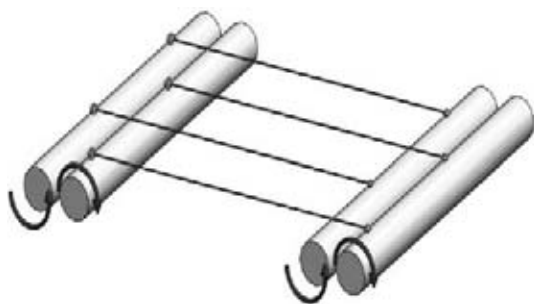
Поперечная резка проволоками совершающими возвратно-поступательные движения
